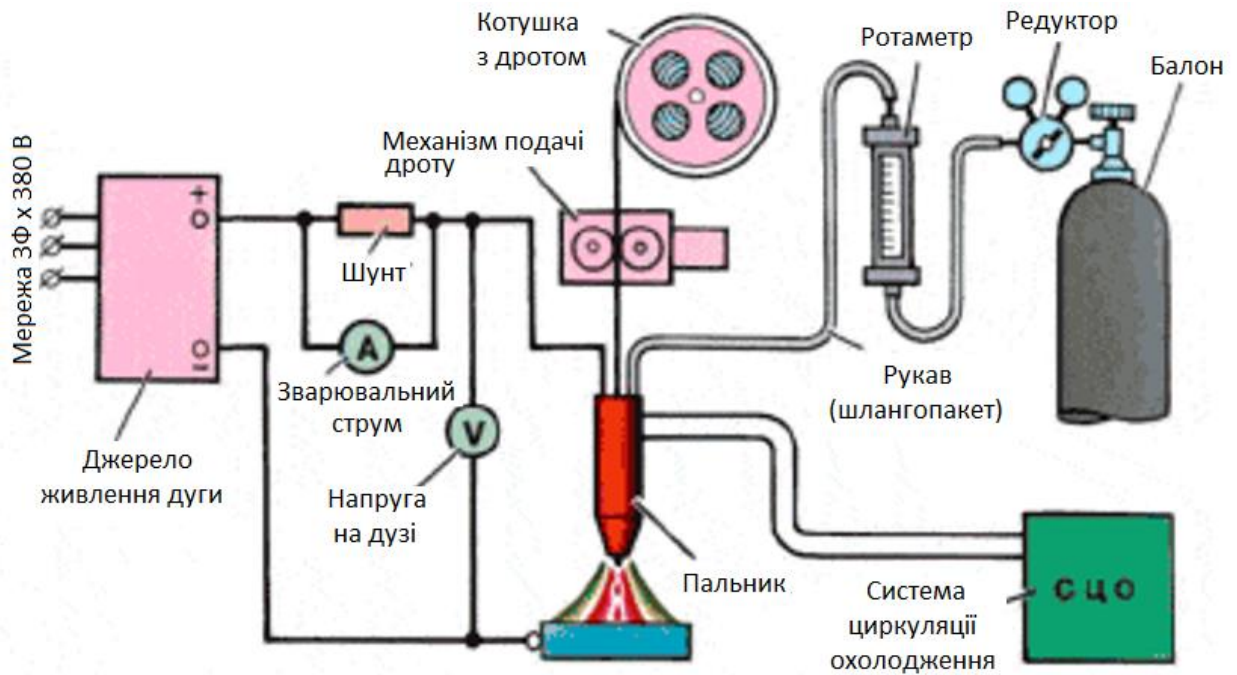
Схема установки для зварювання в середовищі захисних газів
